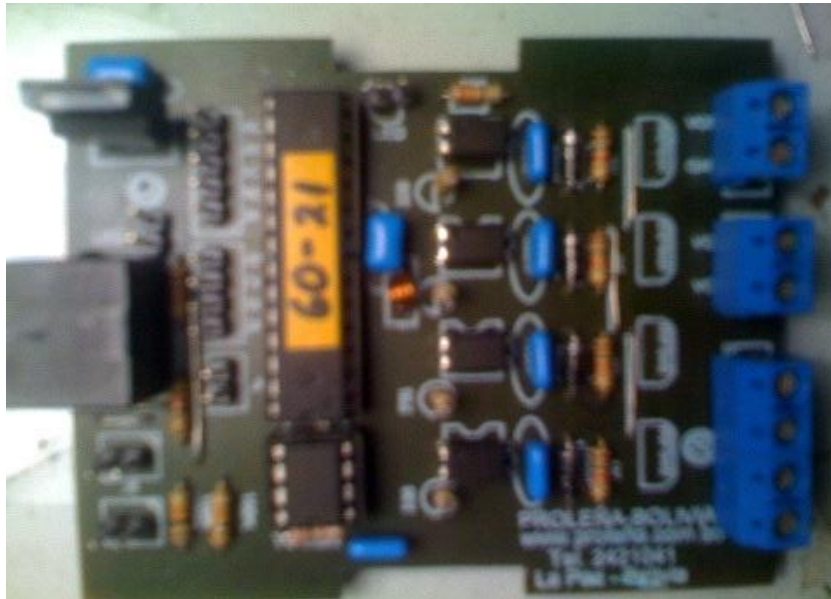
CIRCUITO PCB FINAL PERIFÉRICO MP
